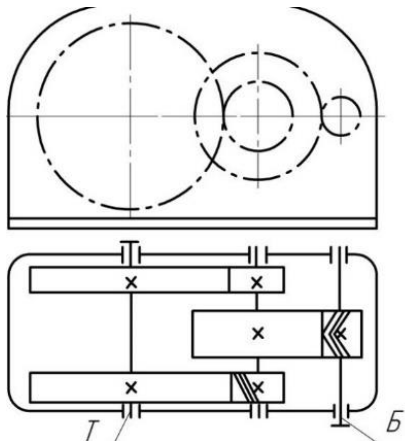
Двухступенчатый горизонтальный редуктор с раздвоенной тихоходной ступенью
